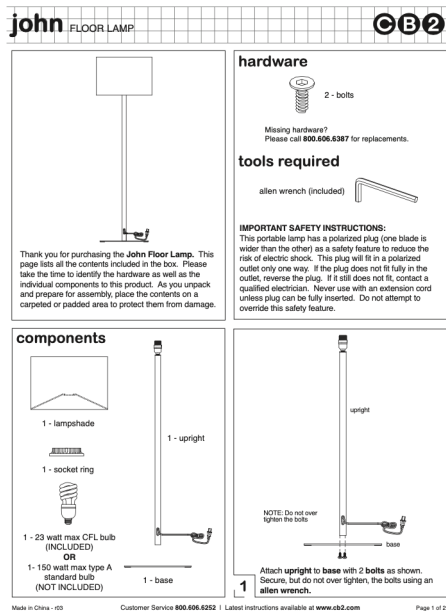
Instruções de montagem do *John Floor Lamp*, da CB2. O esquema evidencia a estrutura fundamental do objeto, composta por base, pé e difusor, reforçando a clareza construtiva e a organização modular que caracteriza a sua tipologia.
